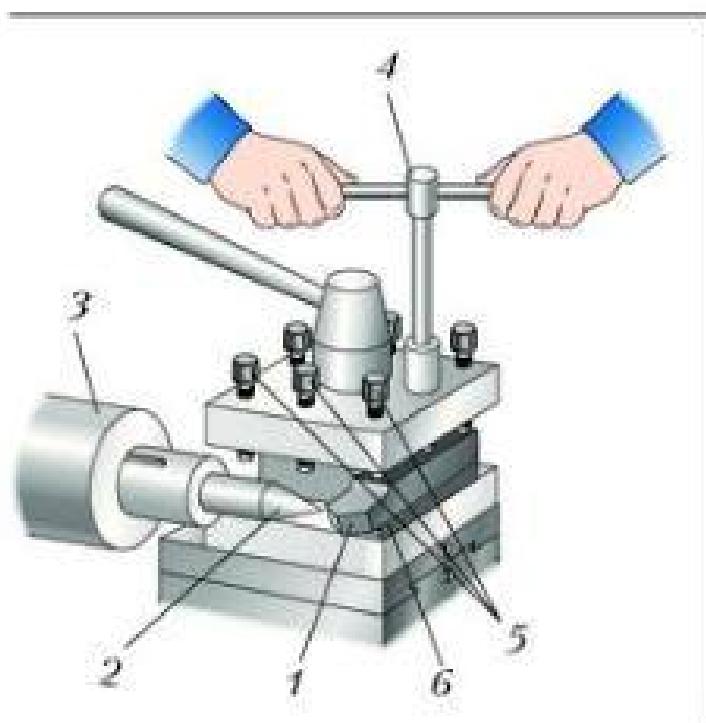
Установка токарного резца в резцодержателе: 1 — резец; 2 — задний центр; 3 — пиноль задней бабки; 4 — ключ; 5 — винты крепления резца; 6 — подкладки под резец
